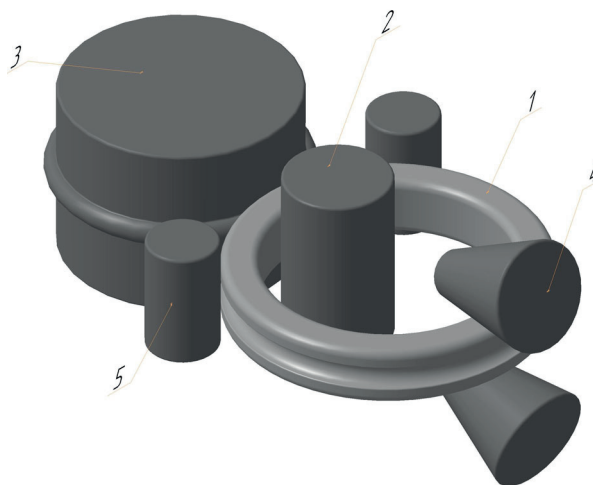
Схема кольцераскатки: 1 – кольцевая заготовка; 2 – внутренний валок; 3 – внешний валок; 4 – комплект осевых валков; 5 – комплект направляющих валков
